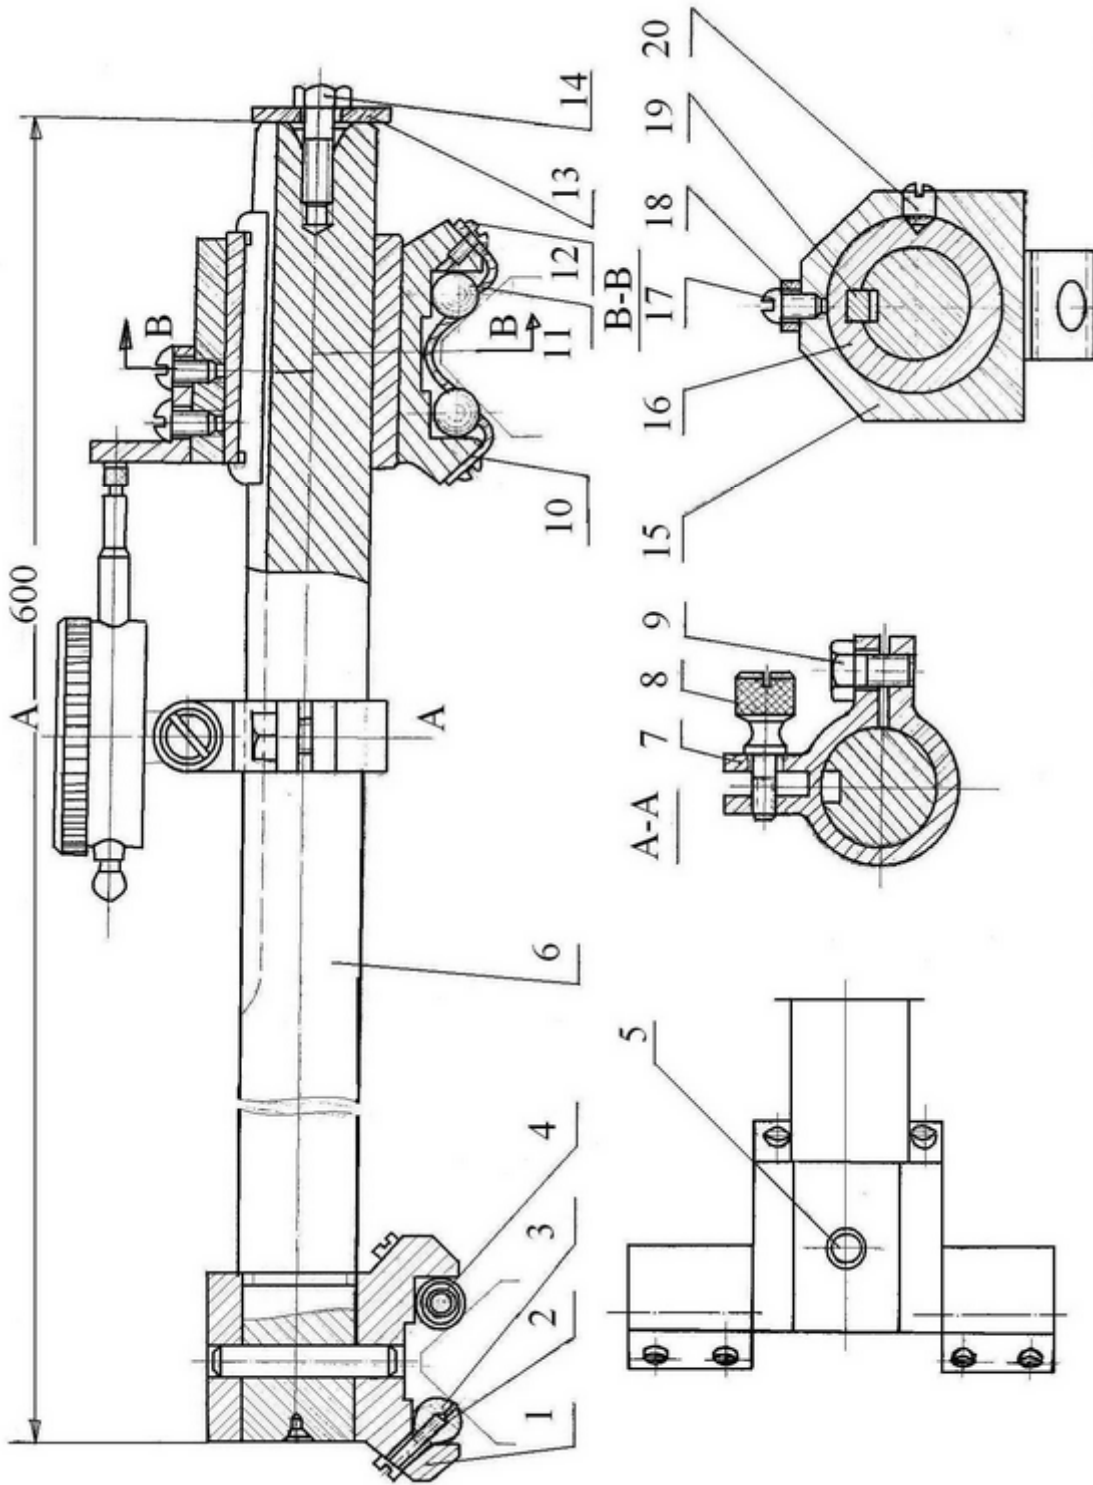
Приспособление для проверки параллельности направляющих станины СД 8532 – 4008
